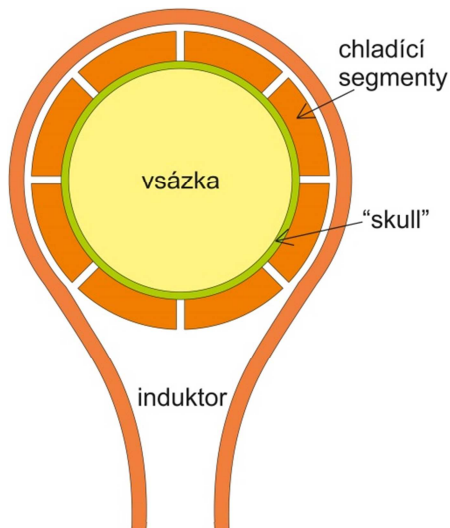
Rozdíl mezi segmentem a trubicí (elementem)
